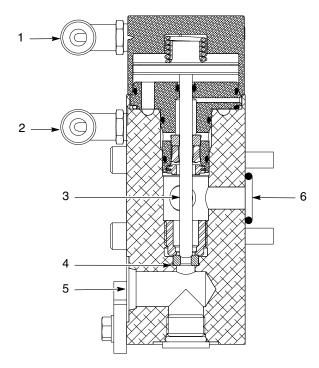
Schnittansicht, Einlassventil der S-Serie
